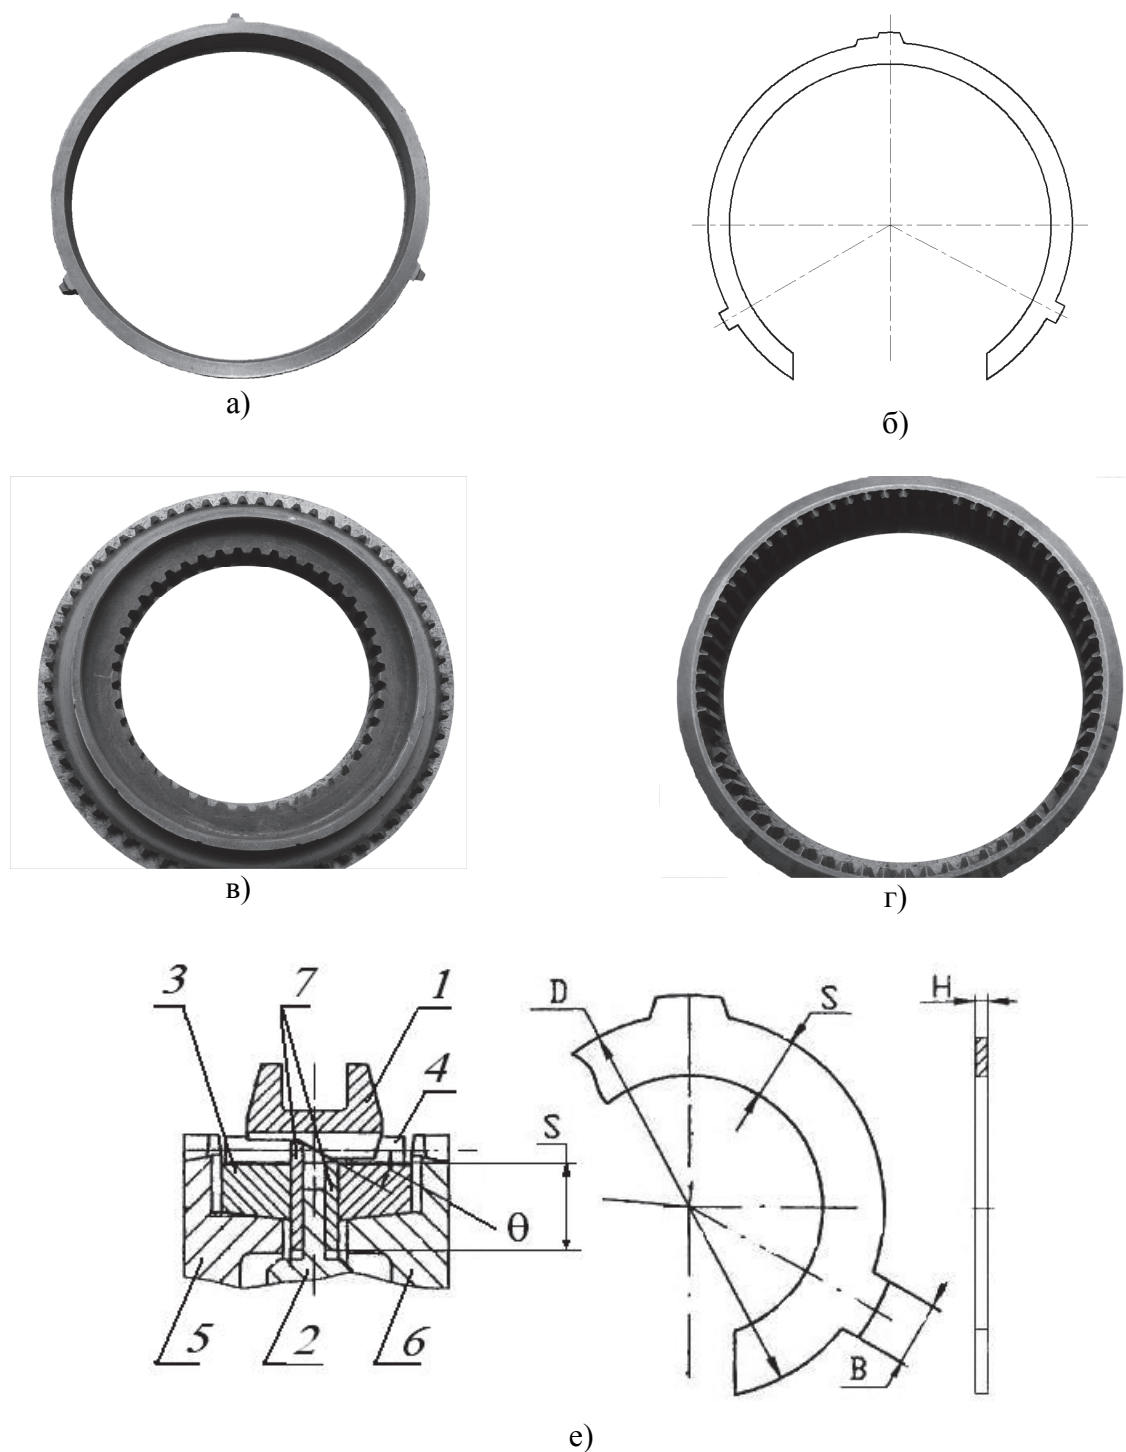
Бессухарный синхронизатор с пружинными кольцами
